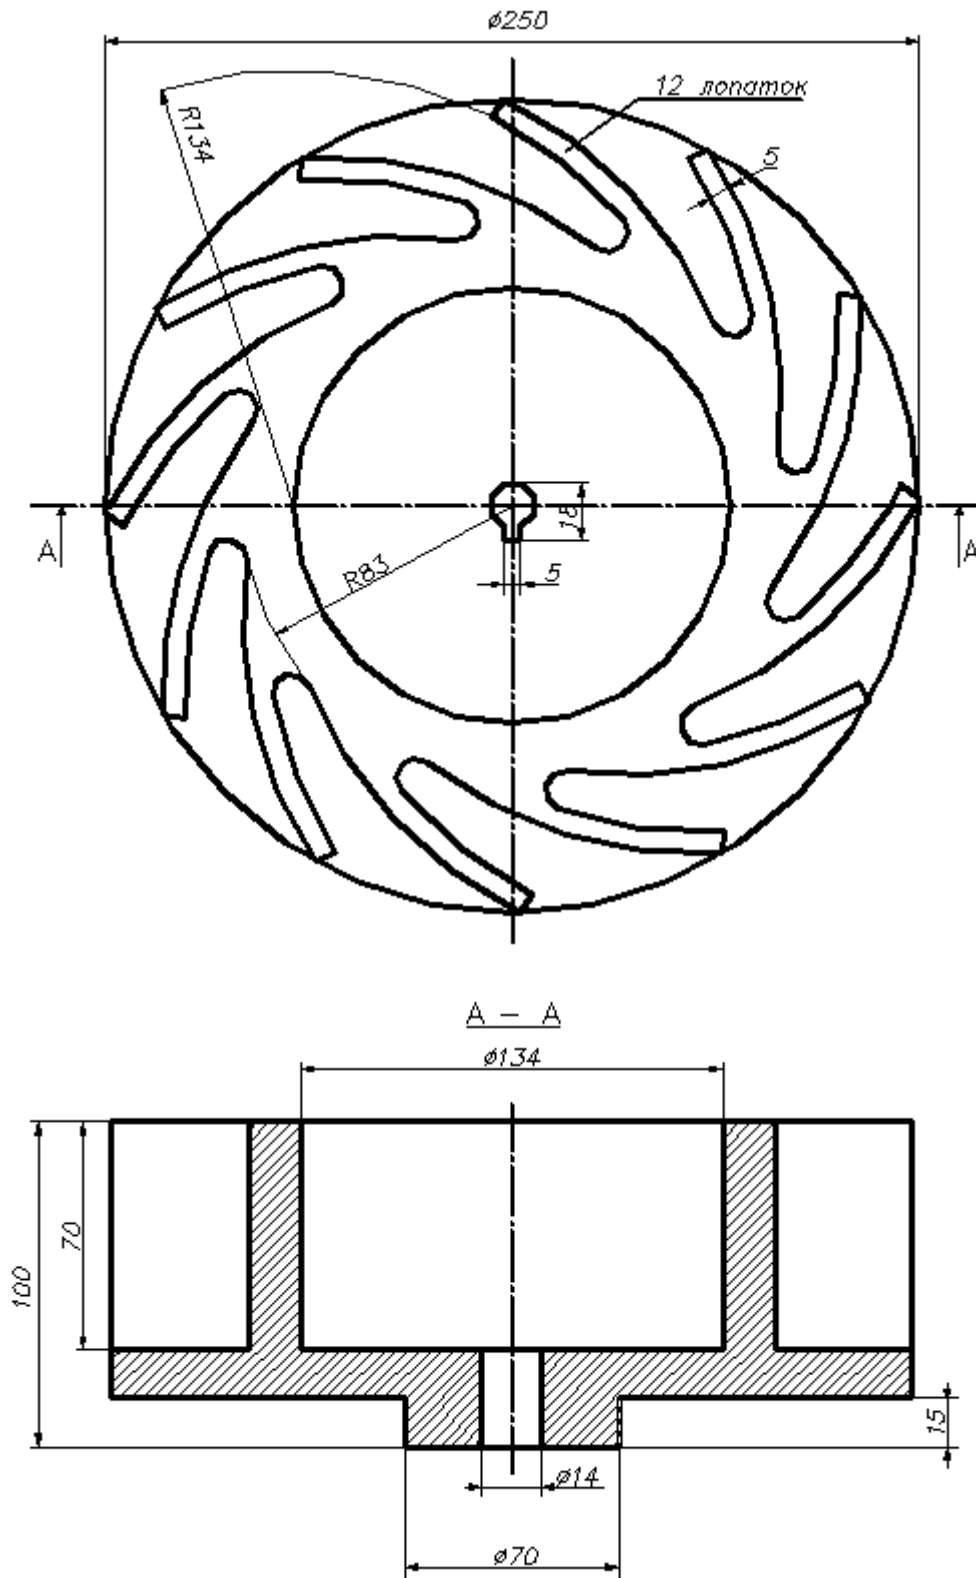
Чертеж рабочего колеса вентилятора мод. КС-54 АТП9.122.0301
